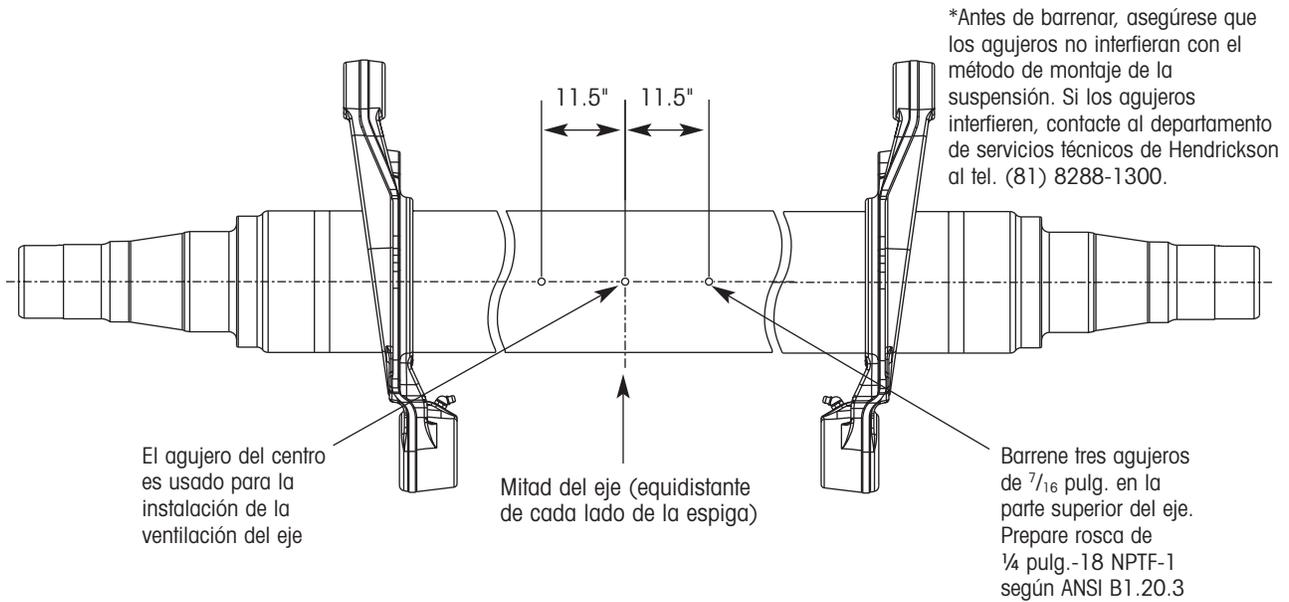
Detalles de barrenado para Ejes Hendrickson para Remolques
